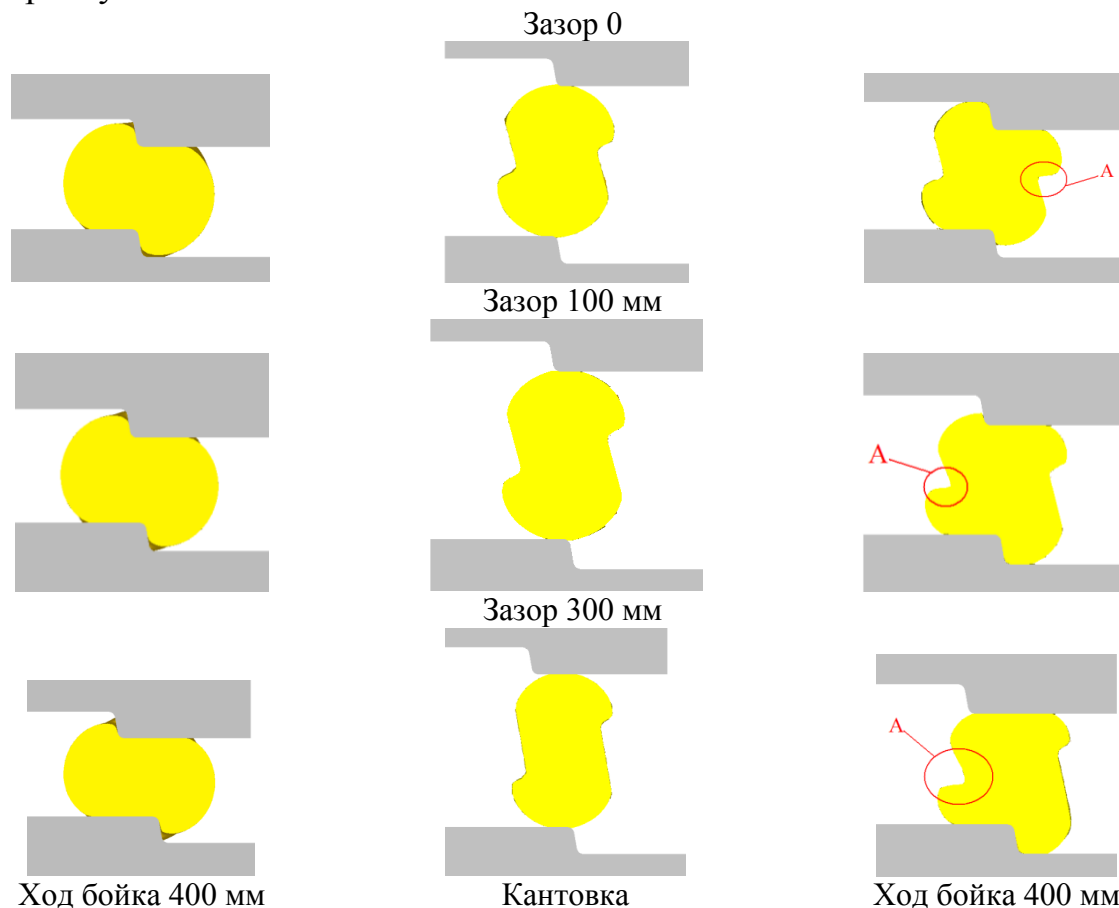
Формоизменение поперечного сечения заготовки при ковке ступенчатым бойком с различным зазором и высотой уступа 200 мм
